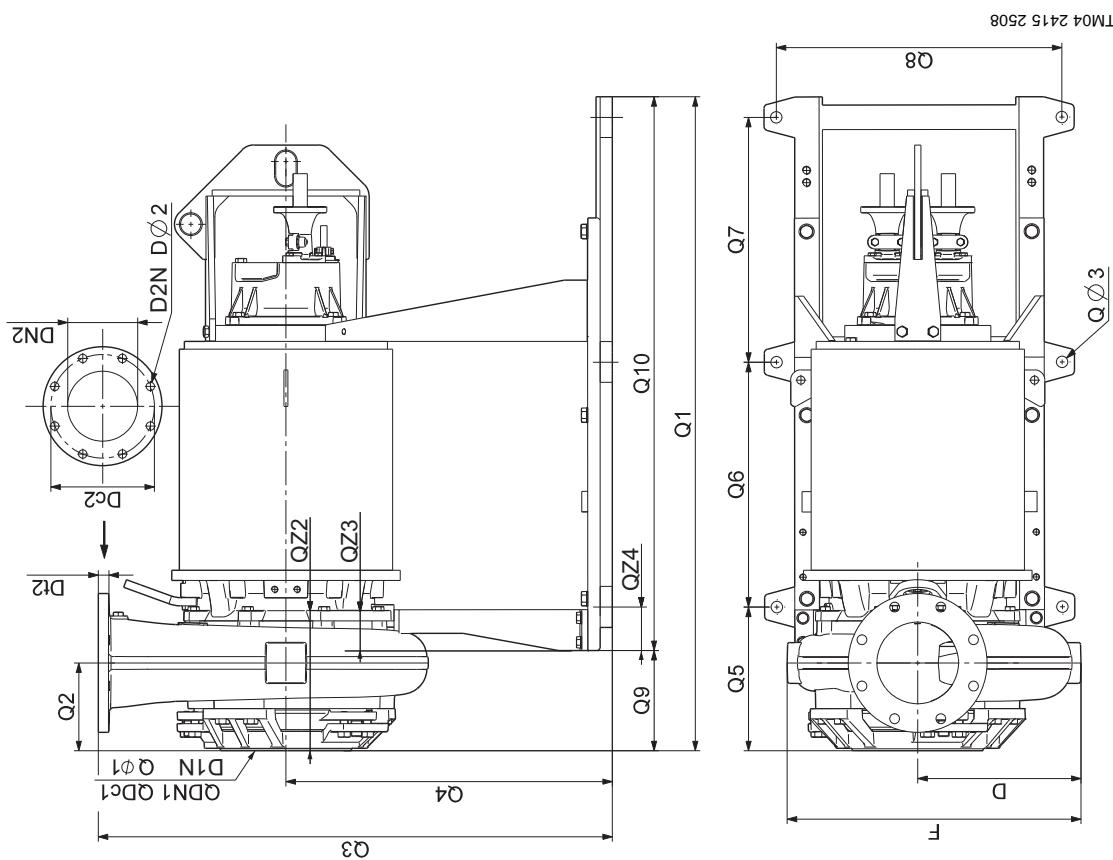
Габаритные размеры, сухая горизонтальная установка на опоре
